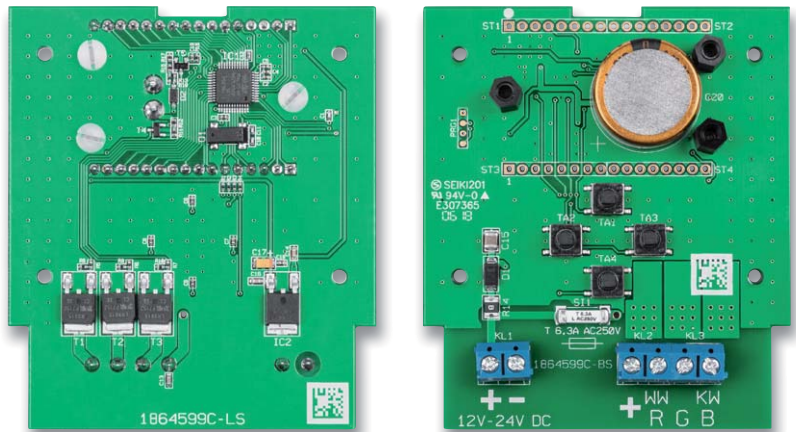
Die mit Schraubklemmen, Goldcap und Abstandhaltern bestückte Platine. Links sieht man die von unten eingesetzten Kunststoffschrauben.
